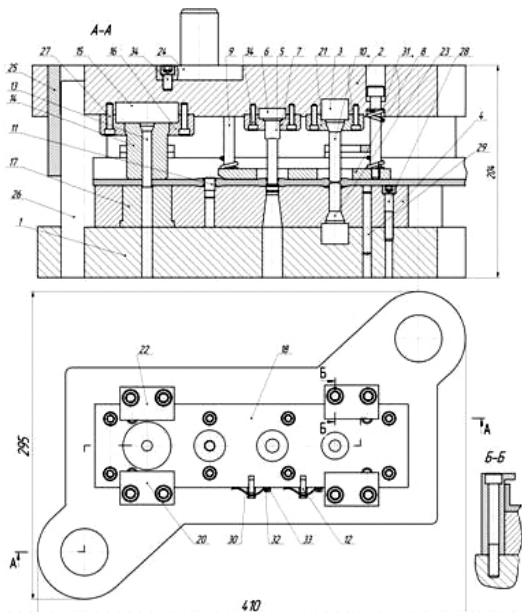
Конструкция штампа для интенсивного упрочнения металла в алюминиевом профиле
